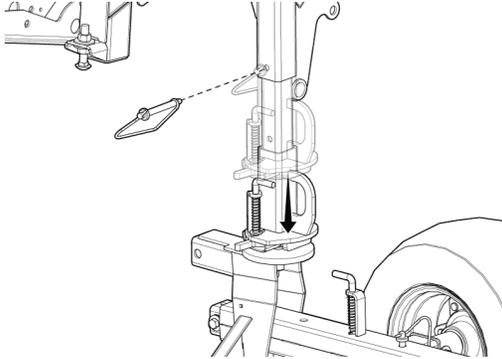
Deichselhalterung auf Drehschemelachse absenken
